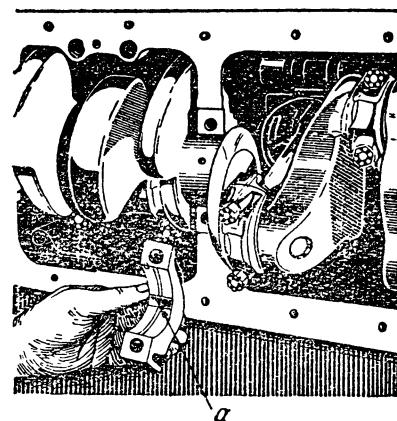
Проверка радиального масляного зазора в коренных подшипниках с помощью калиброванной пластины
